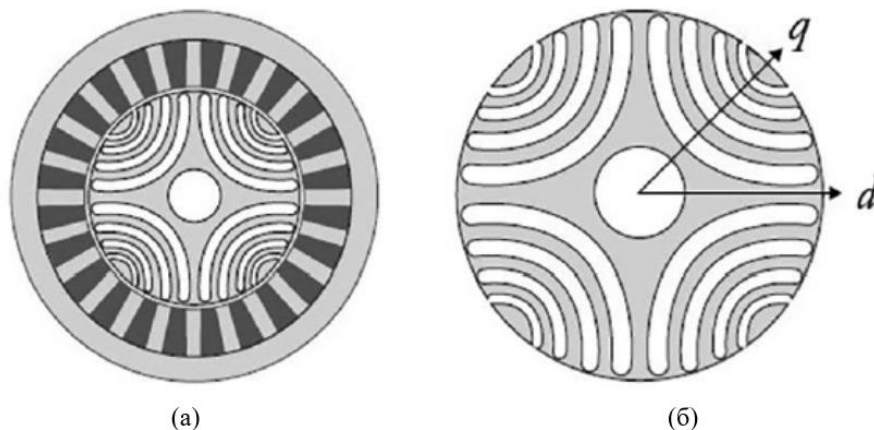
Синхронный реактивный двигатель: а – СРД в поперечном разрезе, б – одна из конструкций ротора СРД
